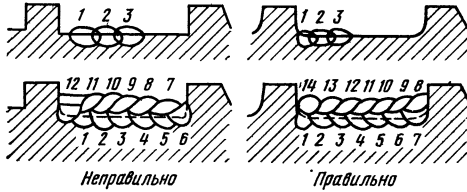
Заклинивание шлаковой корки при неправильной технике наплавки. Цифры указывают порядок наложения наплавленных валков
